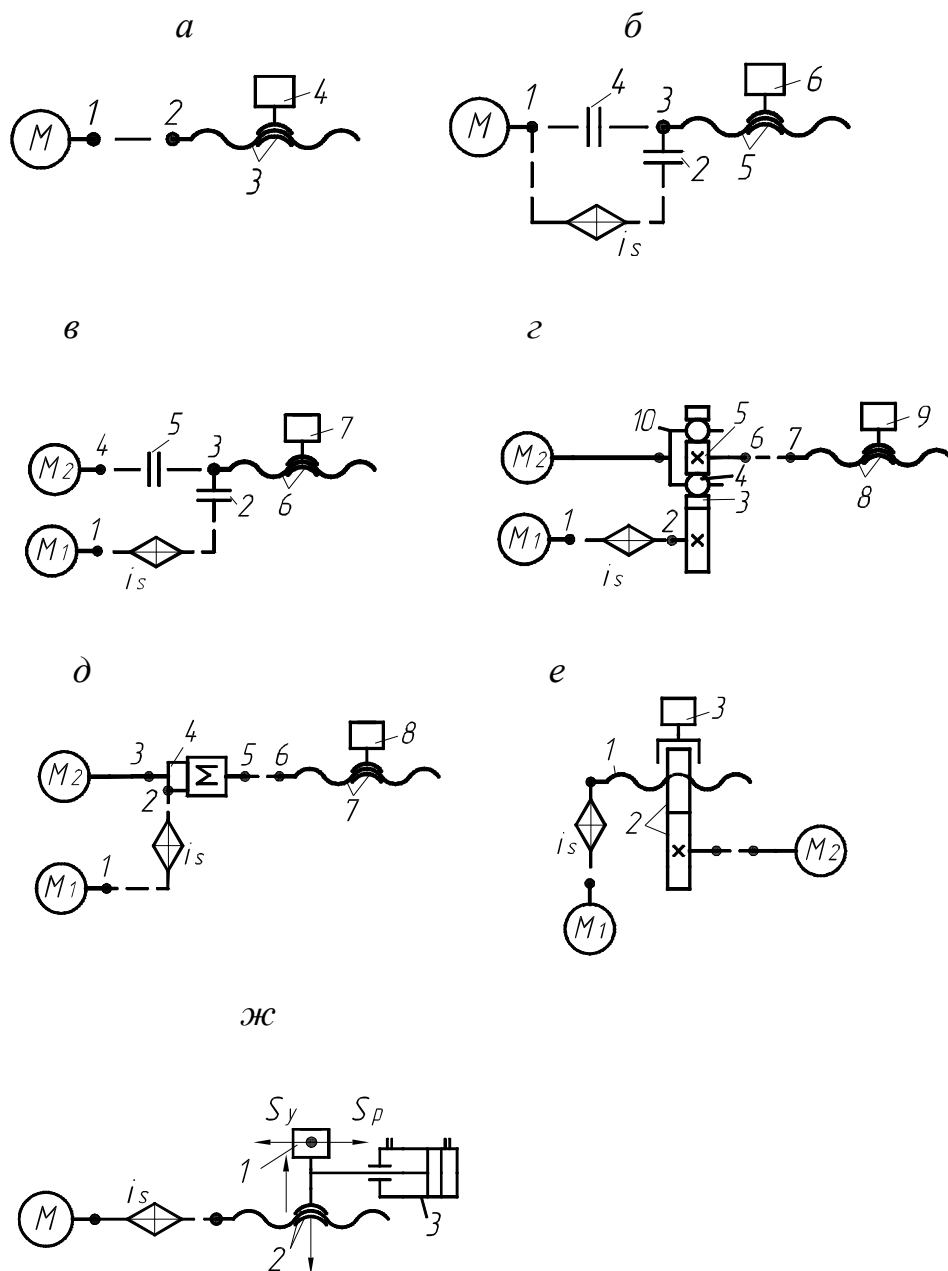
Схемы приводов подач с рабочими и ускоренными перемещениями: а, б – с общим двигателем; в – е – с отдельными двигателями; ж – с двумя тяговыми устройствами
